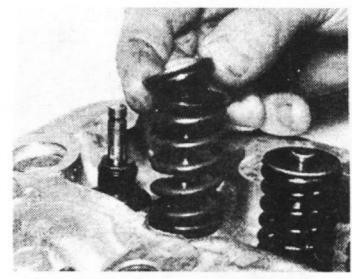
Установите пружину и чашку пружины поверх штока клапана...
